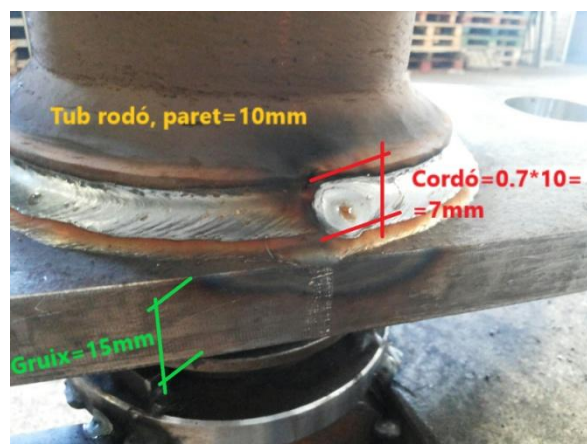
1. Exemple del cordó de soldadura màxim.
